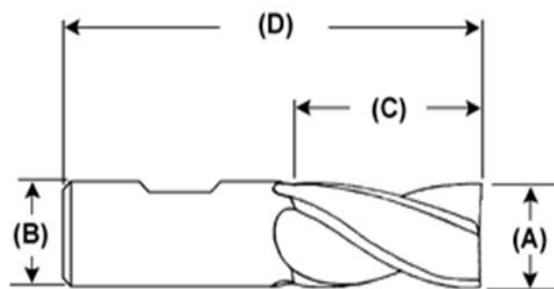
Конструкция концевых фрез А-диаметр фрезы ;
